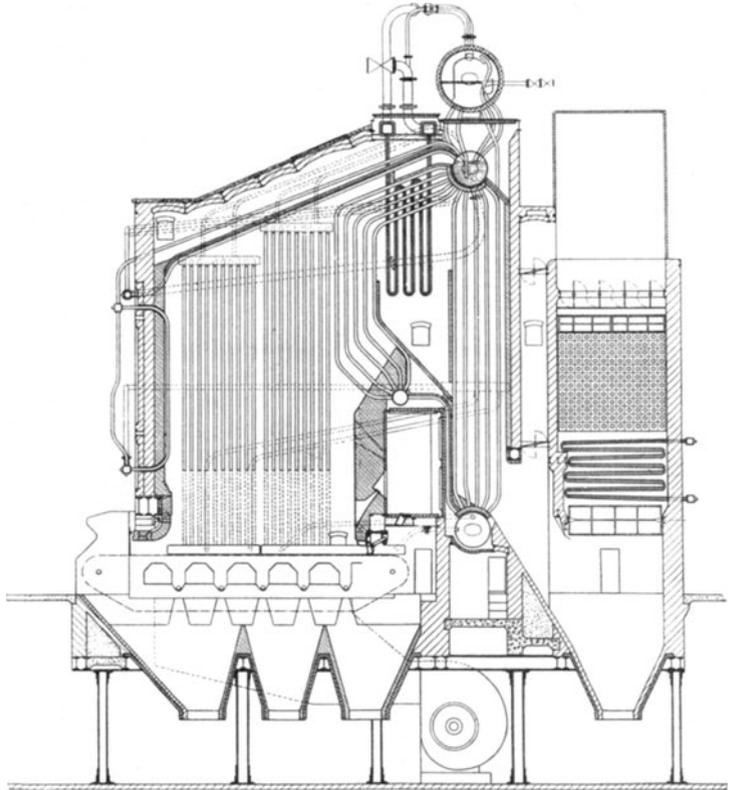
Hochleistungs-Steilrohrkessel der Firma Steinmüller, Gummersbach, 555 m<sup>2</sup> Kesselheizfläche, Zonenwandroost mit Unterwind, dem Rippenrohrkonominer ist ein Schlangenrohrkonominer als Verdampfungsvorwärmer nachgeschaltet. Die oberste, mit Isolierstoff verpackte Trommel außerhalb der Kesselzüge ist kein Dampfhammer, sondern eine Speichertrommel (D.R.P.), deren Wasserpiegel ohne Gefährdung der Betriebssicherheit bei vorübergehenden Störungen der Kesselspeijung völlig abgesenkt werden kann. Der Feuerraum ist an den Wänden und der Decke mit Kühlrohren im Wasserumlauf verkleidet. Von außen zugänglicher Bedienungsgang über dem Kofstende. Vor den Konominern großer Flugaschen-Abscheidungsraum. Stündl. Kesselleistung bis zu 105 kg/m<sup>2</sup> Normaldampf.
